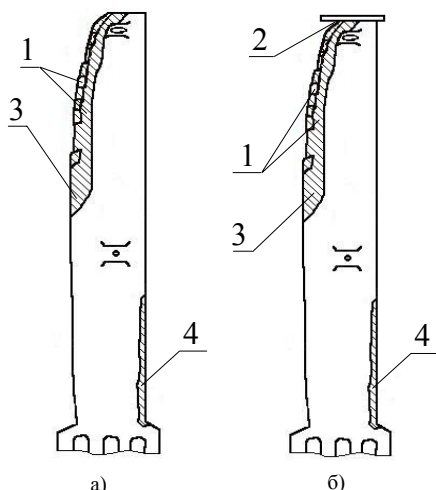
Схема расположения защитно-упрочняющих покрытий на рабочих лопатках: а – профиля 1224; б – профиля 1355
